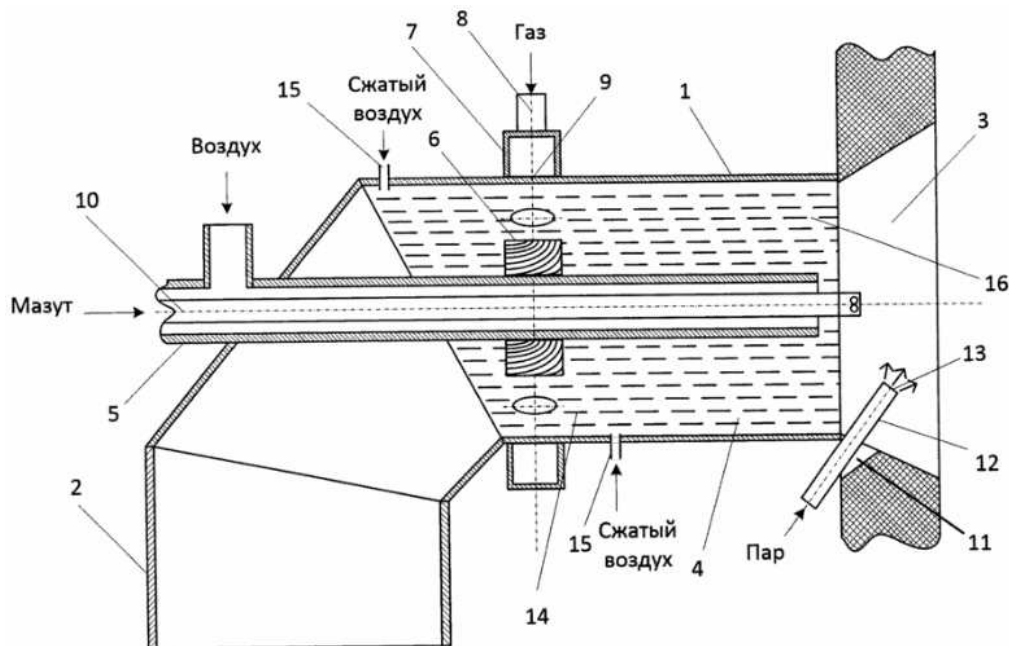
Схема новой газомазутной горелки: 1 – корпус; 2 – патрубок для подачи воздуха; 3 – амбразура; 4 – смесительная камера; 5 – труба; 6 – вставка; 7 – кольцевой коллектор; 8 – патрубок подачи газа; 9 – газораздающие отверстия; 10 – мазутная форсунка; 11 – канал; 12 – паровая труба; 13 – распылитель пара; 14 – разделитель воздушного потока; 15 – впрыск сжатого воздуха
